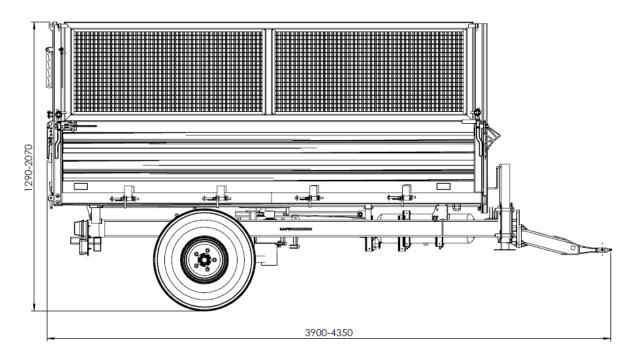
Габаритные размеры прицепа с пневматическим или гидравлическим тормозом - вид сбоку
